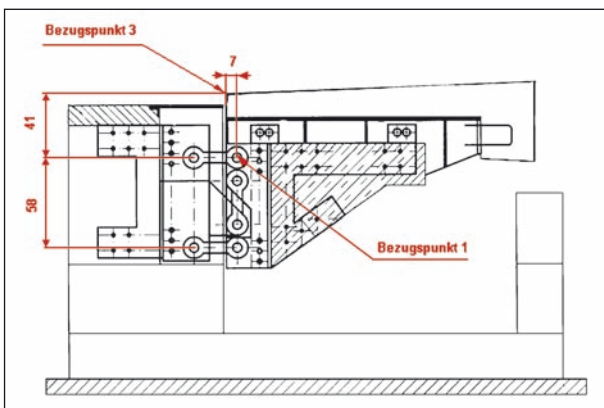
Kragarm der Messbrücke und Lage des Bezugspunktes 1
